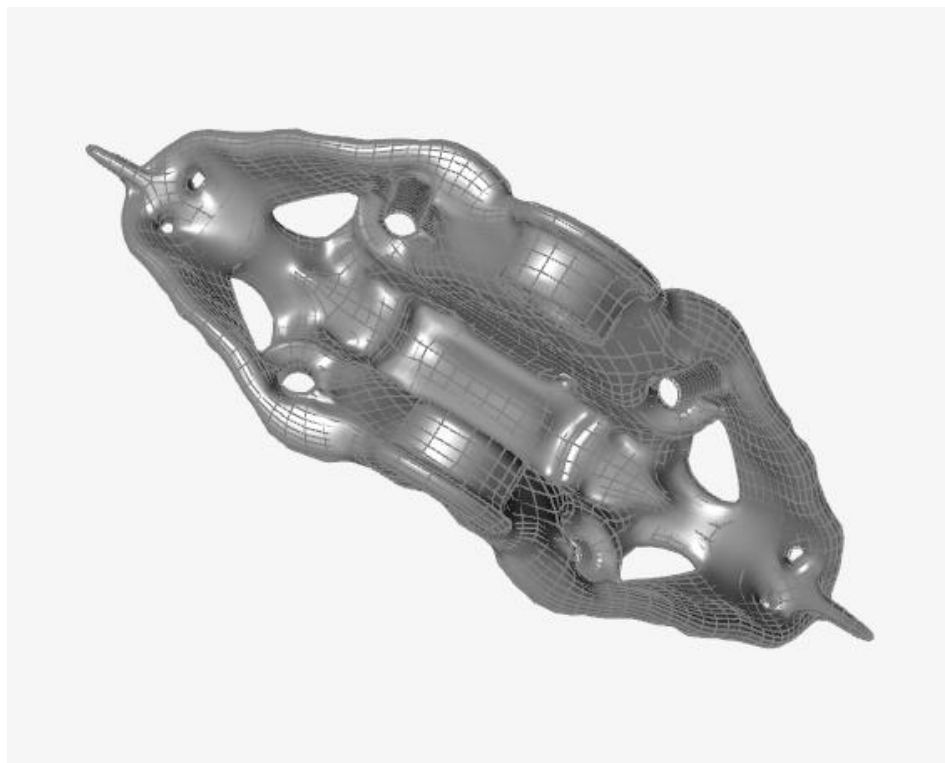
Detalle refinamiento (1). Fuente: elaboración propia
